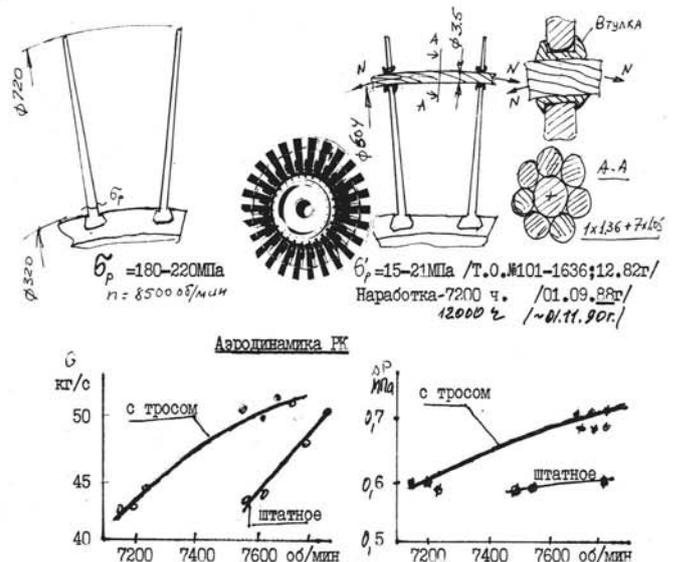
Бандаж рабочего колеса первой ступени компрессора НК-12СТ тросом
